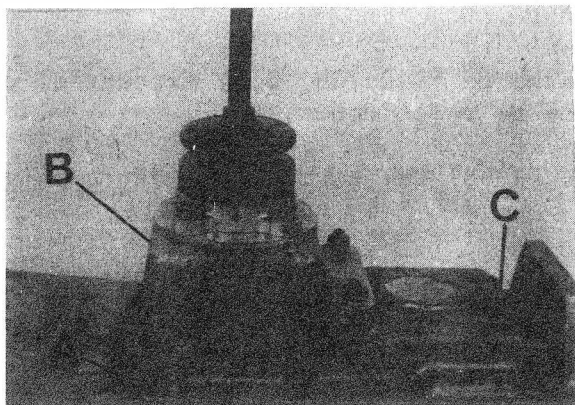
Desmontaje tapa de ejes y horquillas selectoras
